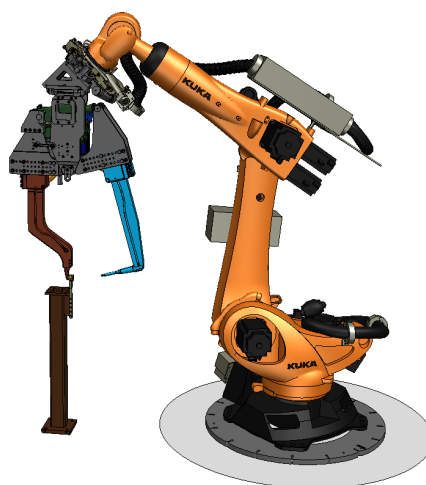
Положение для калибровки сварочного пистолета робота 5080R02 Z
